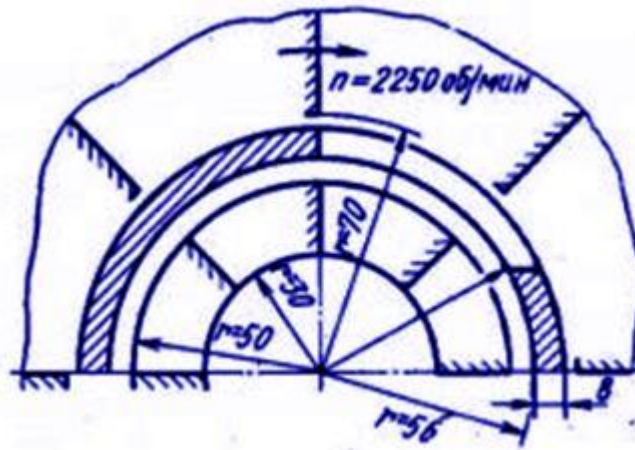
Розміри імелера типового дробометного колеса
